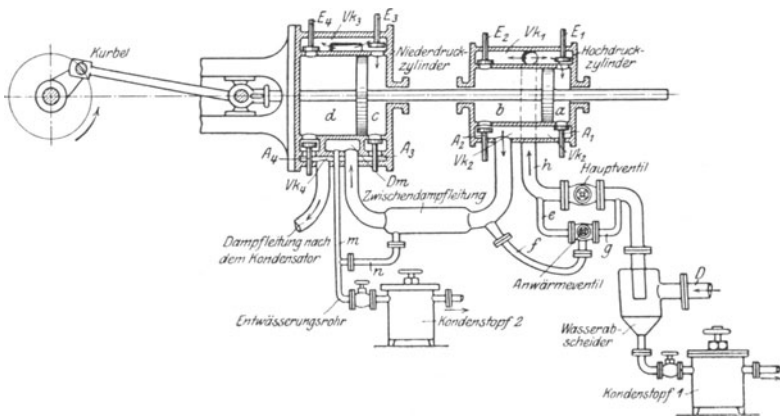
Anwärmschema einer Tandemmaschine mit nur einem Anwärmeventil (Dreivegeventil g).
